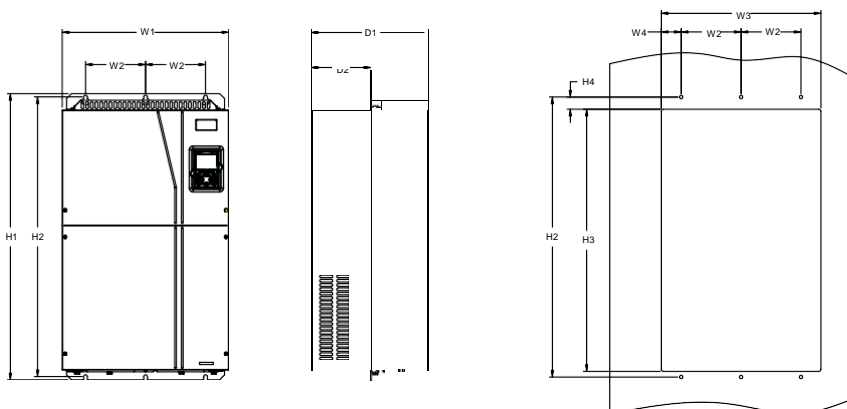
Схема фланцевого монтажа ПЧ напряжением 380 В, от 132 до 200 кВт
